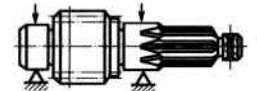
Эскиз обрабатываемого цилиндрического зубчатого колеса типа «вал»:
